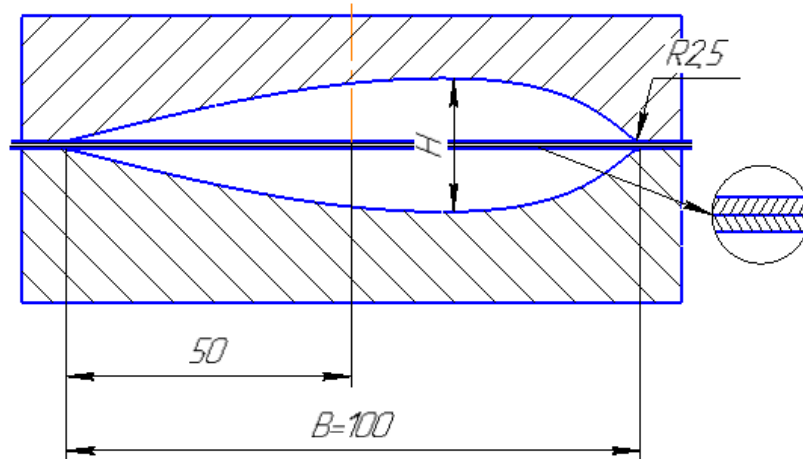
Габаритні розміри порожнини для формоутворення фрагменту порожнистої лопатки
